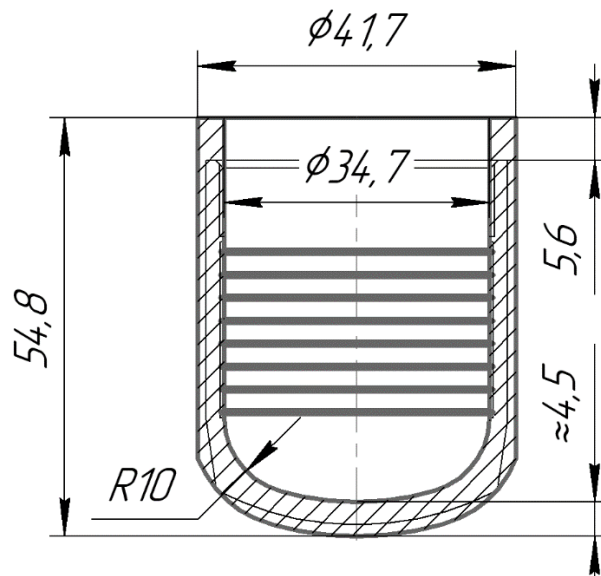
Ескіз заготовки, що отримується після витягування з накладеним контуром кінцевої деталі
